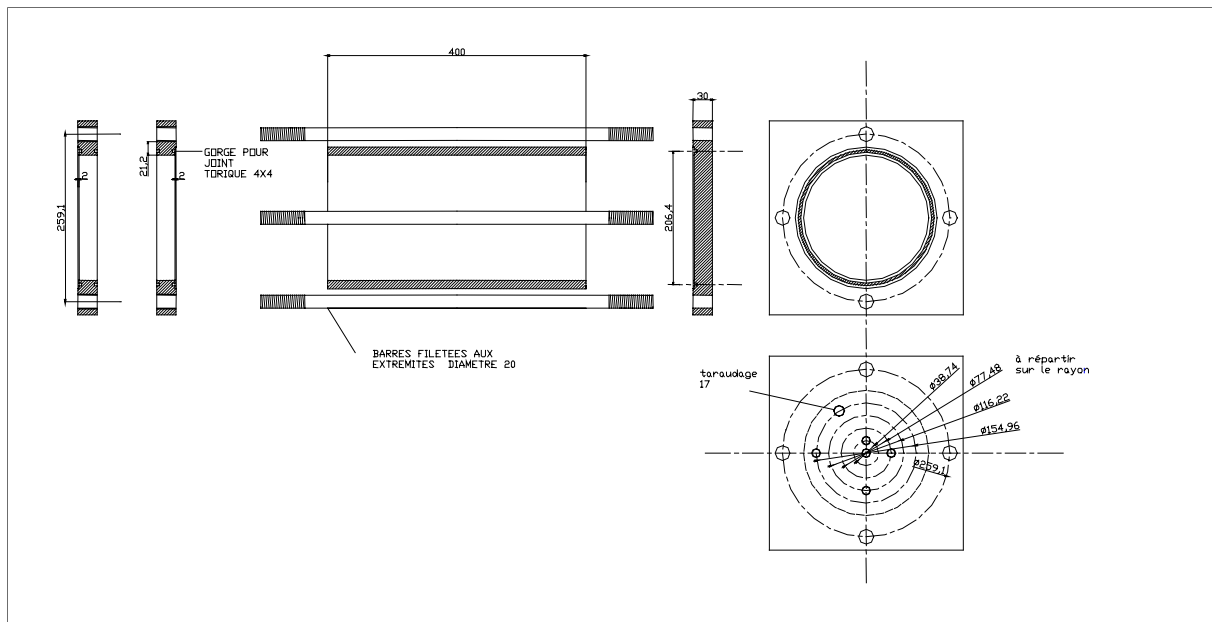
Plan du tube 2, des brides joignant les deux tubes et de la bride arrière.
